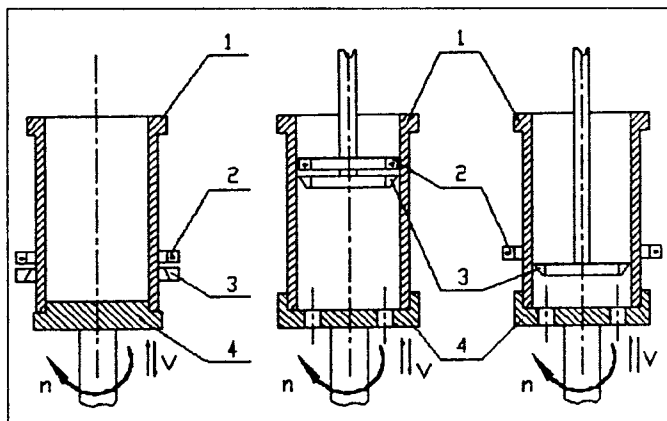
Способы восстановления гильз цилиндров ТПД без матрицы: 1 — гильза; 2 — индуктор; 3 — спрейер; 4 — оправка
